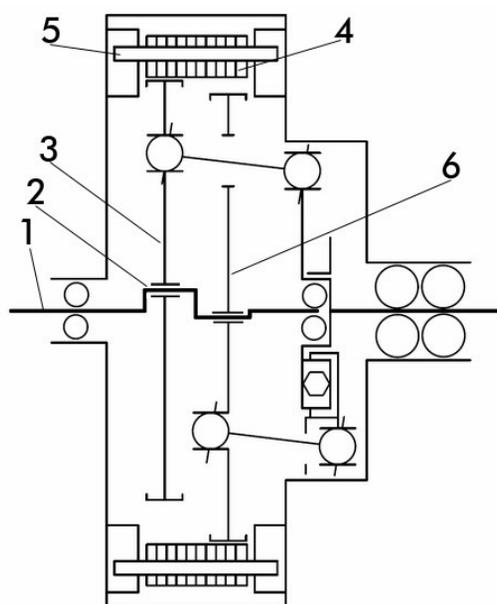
Схема уравнивающего механизма с двумя сателлитами и зубчатой цепью, удерживаемой от поворота относительно корпуса
